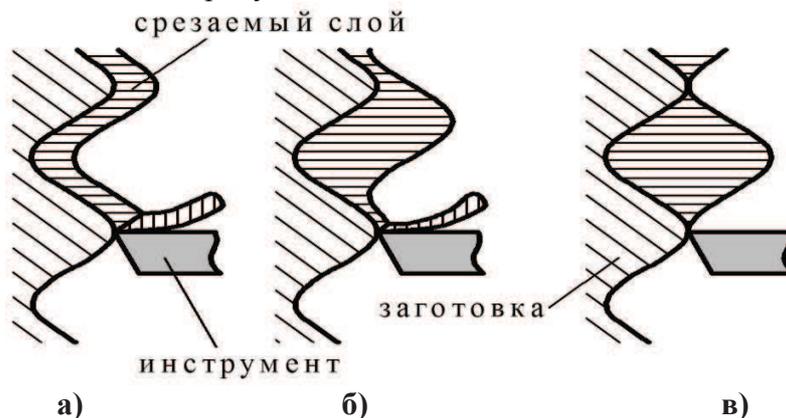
Диссонанс и резонанс автоколебаний заготовки и инструмента [8]
